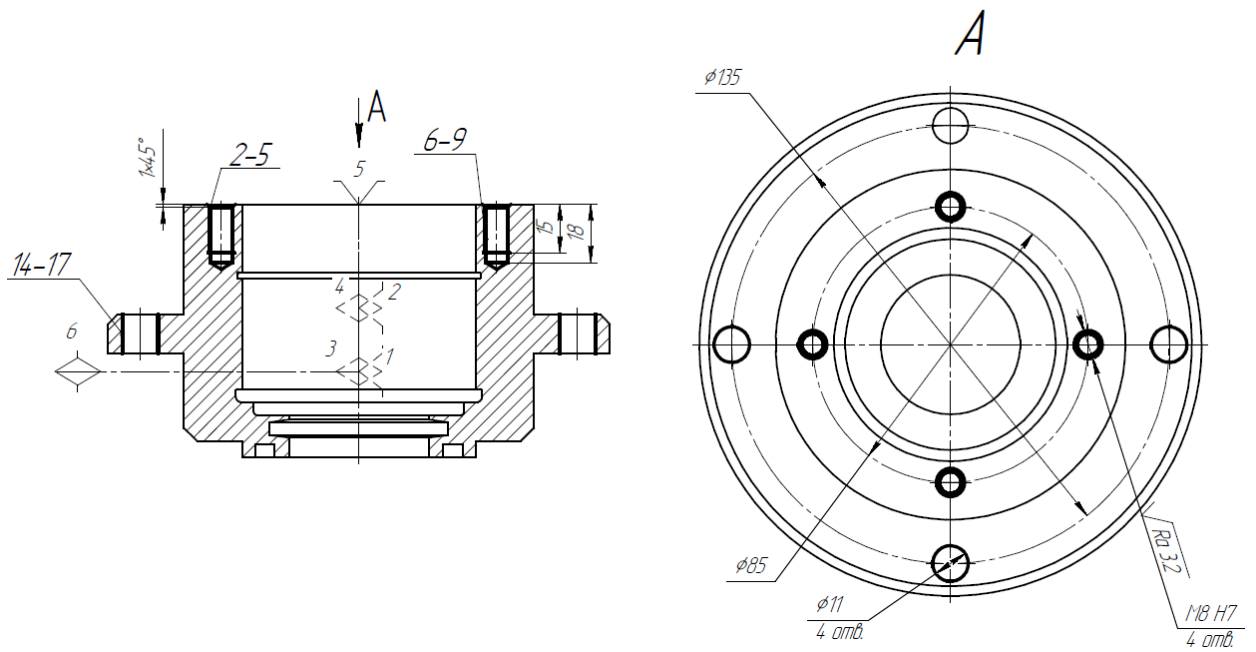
Схема базування та ескізи обробки на операцію 030
